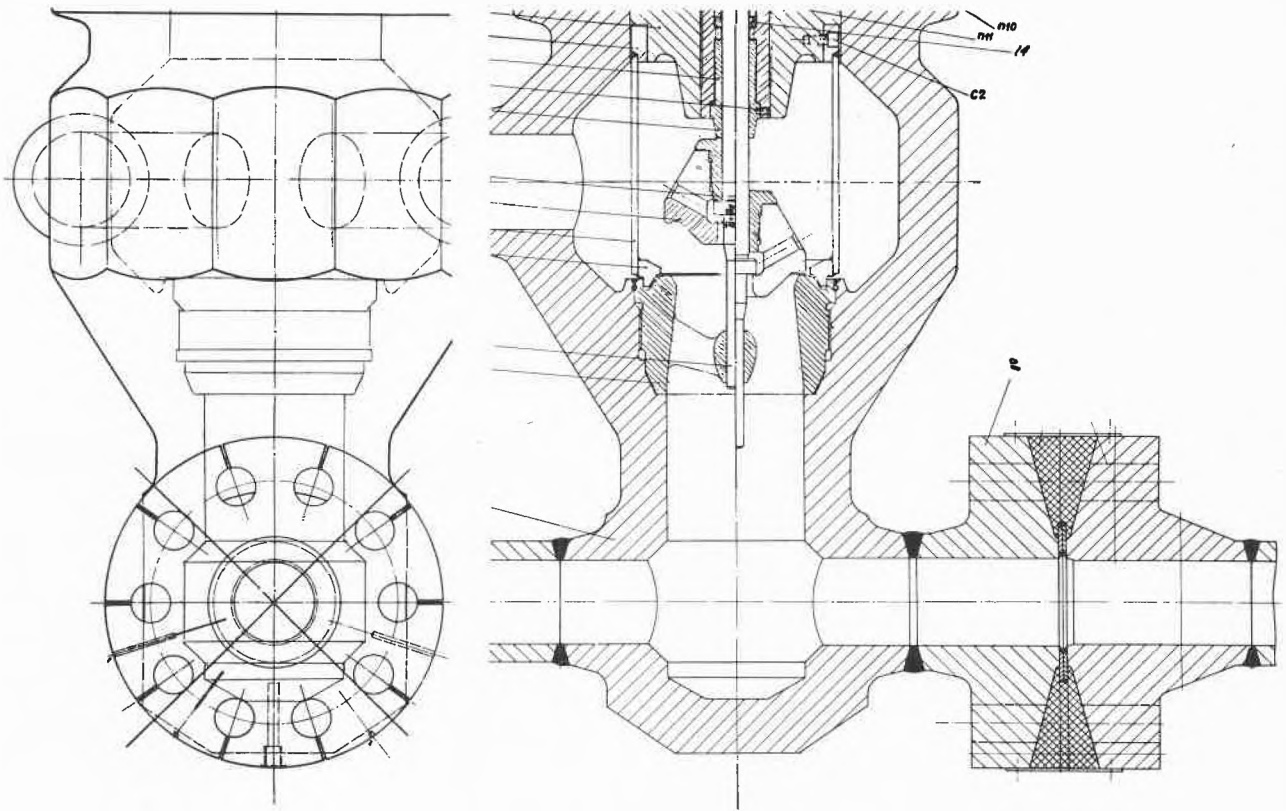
Schnittzeichnung eines Schnellschluß-Absperrventils für 170 at 600°C, Flansch für Rohrleitungsanschluß mit angeschweißten Dichtungsplatten, die nach Zusammenbau am äußeren Umfang dichtgeschweißt werden
